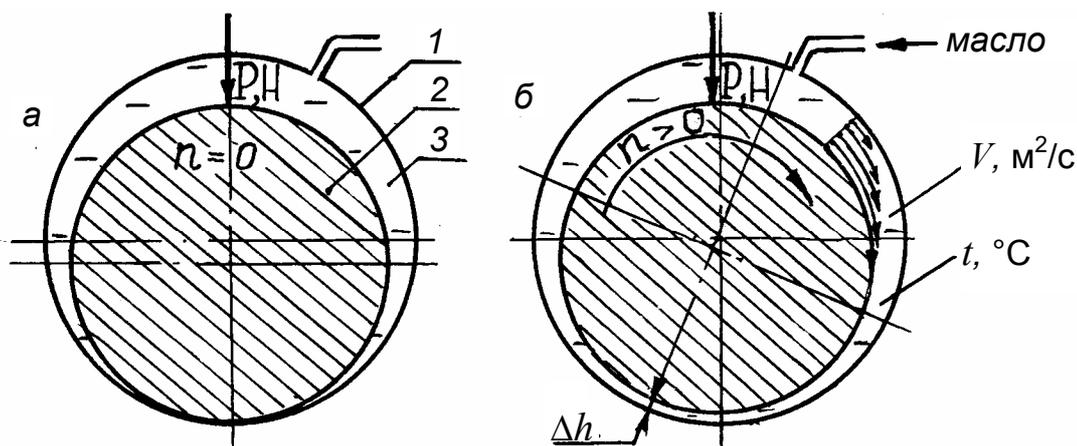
Схема узла с подшипником скольжения: а – с неподвижным валом; б – с вращающимся валом; 1 – подшипник; 2 – вал; 3 – зазор
